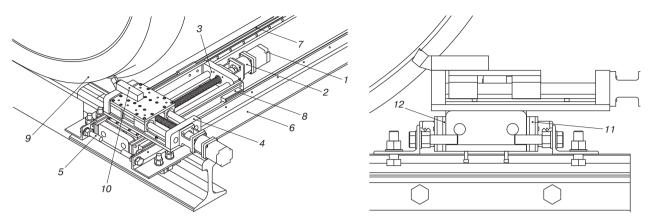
Общий вид станка с ЧПУ для обточки КП [14]:
